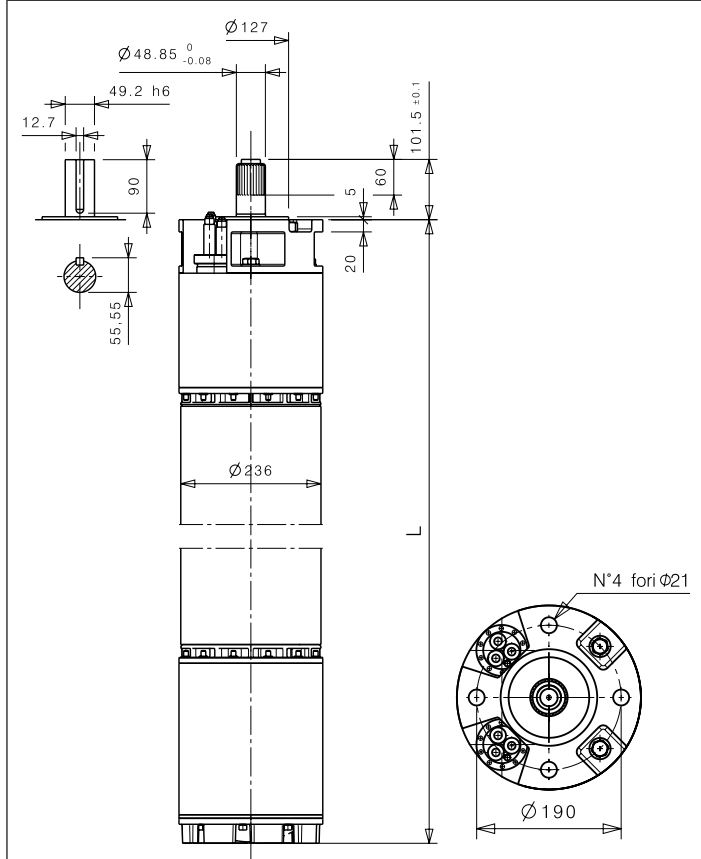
Dimensioni di accoppiamento – Coupling dimensions - Размеры соединения
